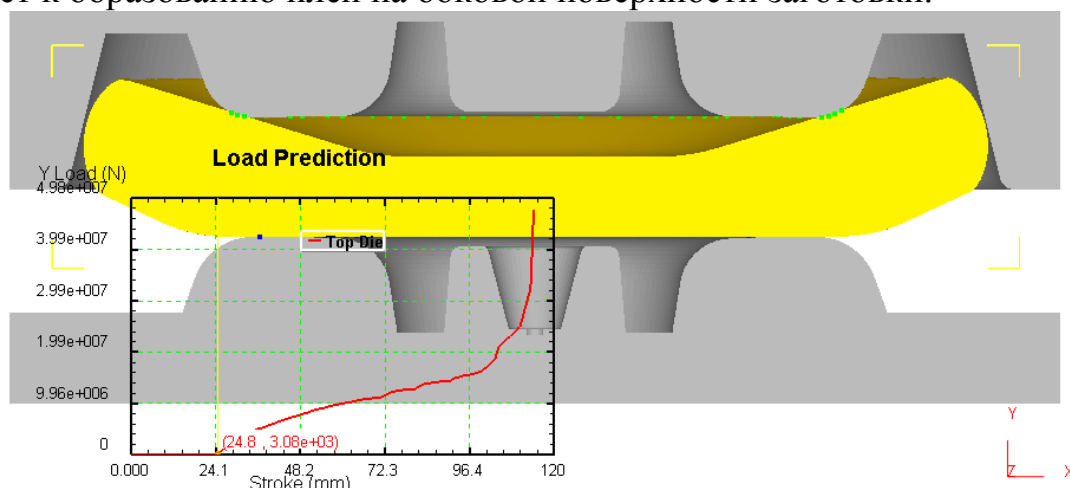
Стадия контакта заготовки со штампами прессы 100МН в зоне будущего диска колесной заготовки на (опыт № 4).
